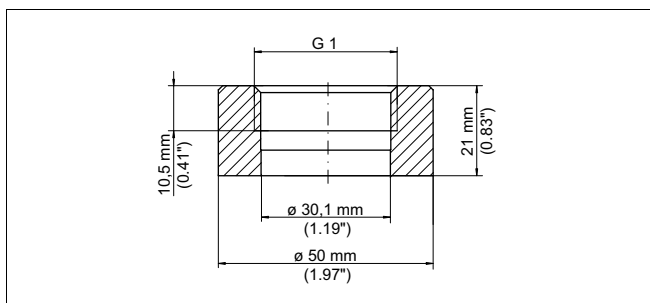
Medidas racor soldado G1 B según ISO 228-1
